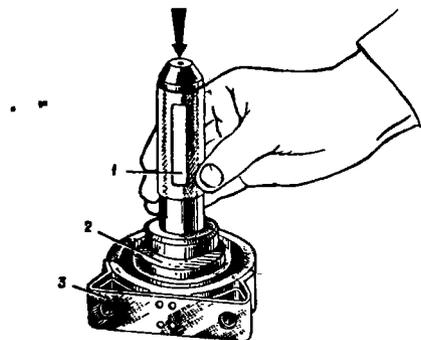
Запрессовка подшипника в упругую опору: 1 - оправка А.70045; 2 - подшипник; 3 - упругая опора
